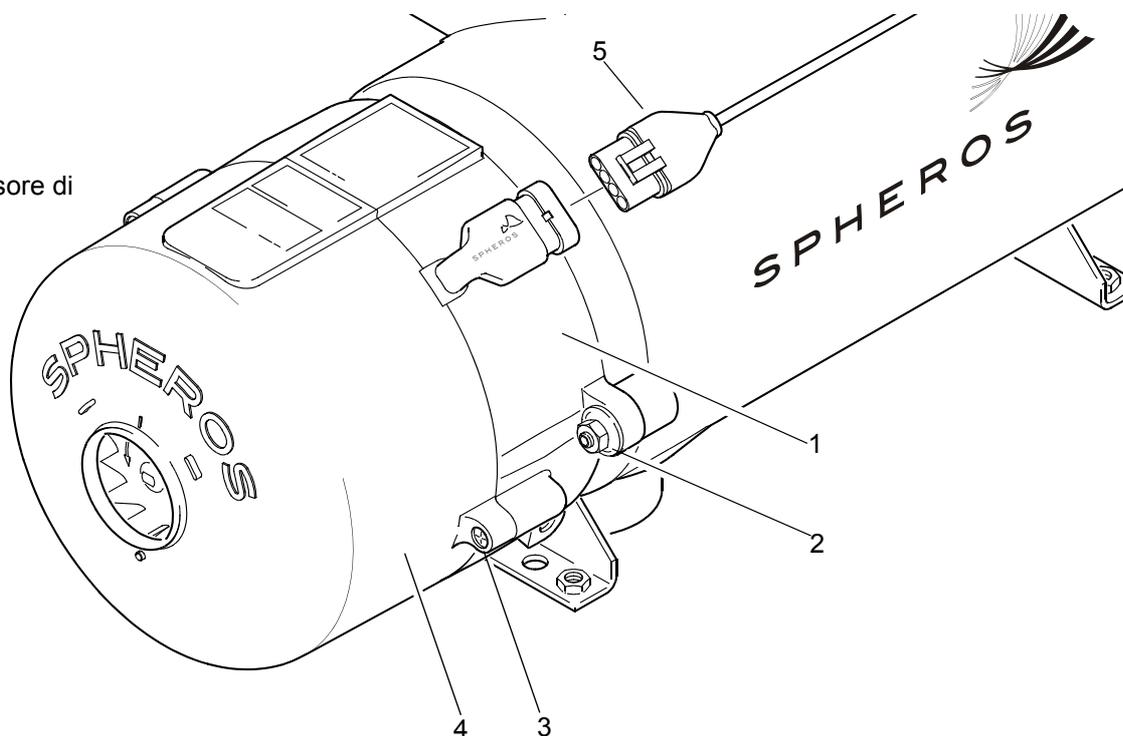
Smontaggio e montaggio della testa del bruciatore / della calotta
